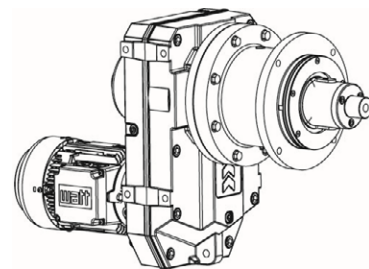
Aufsteckgetriebemotor mit angebauter Lagerlaterne
